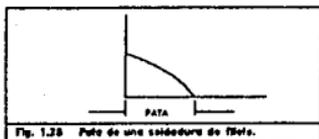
Pata de una soldadura de fibra.
